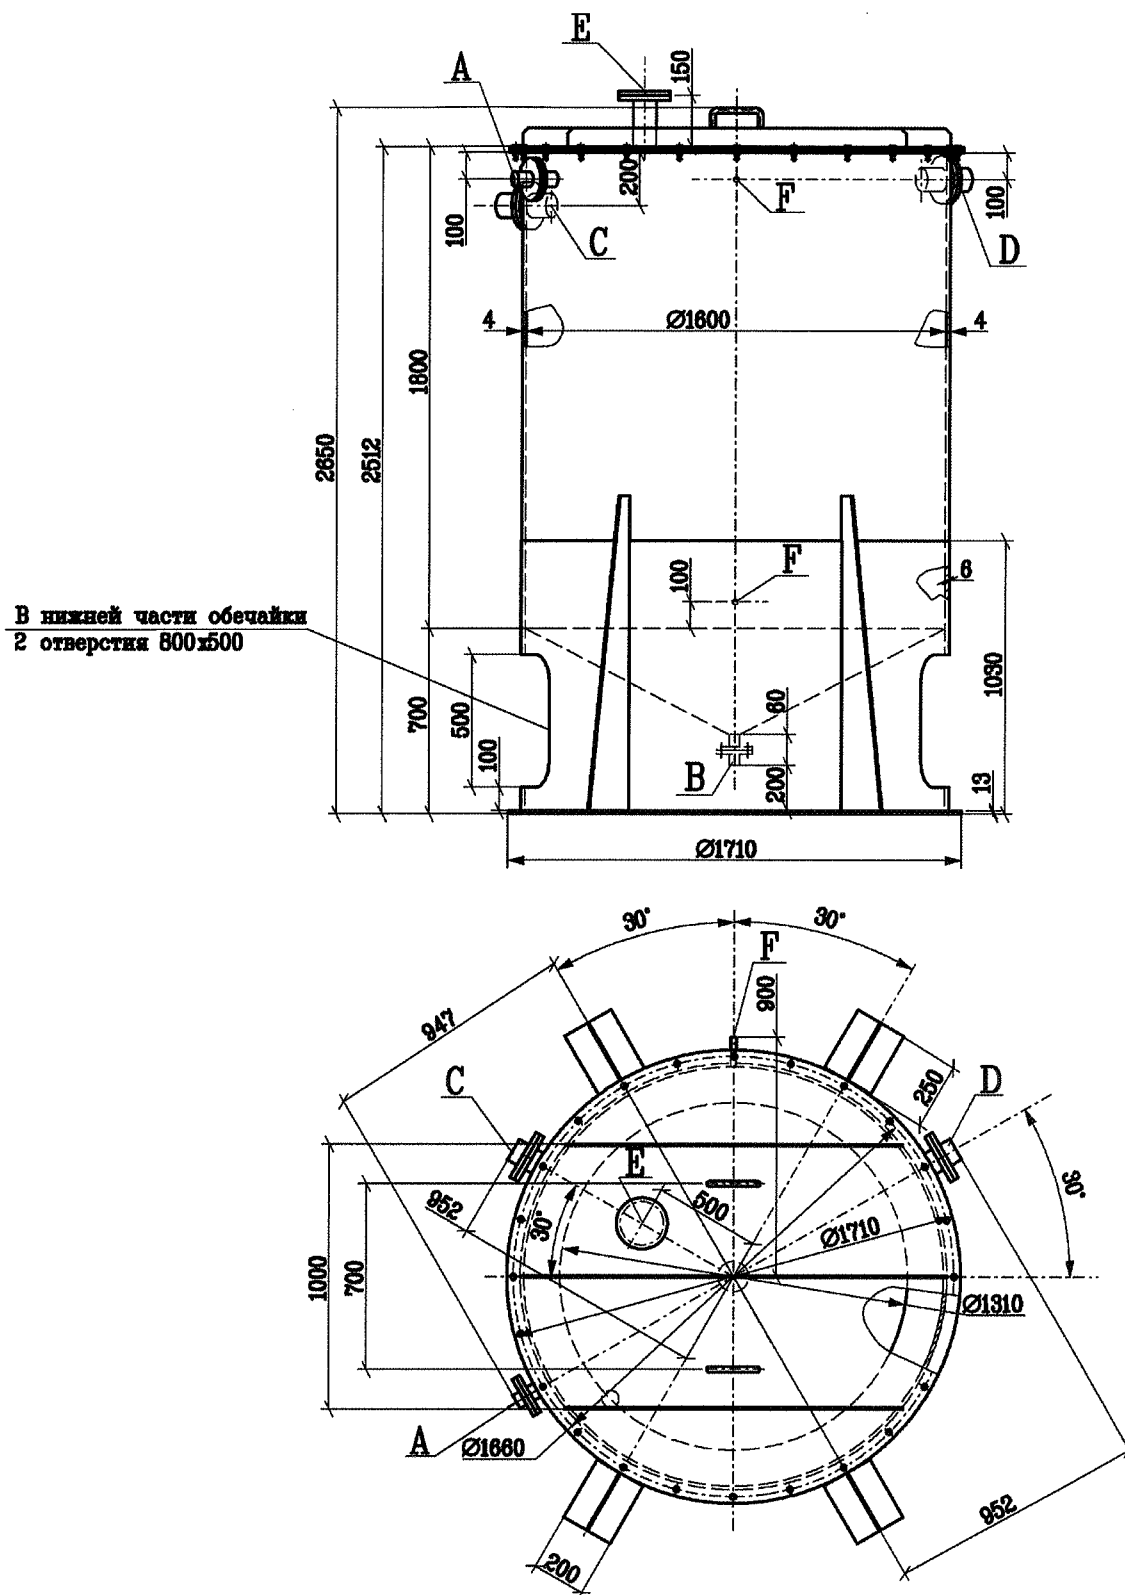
Габаритный чертеж мерников крепкой щелочи и серной кислоты
